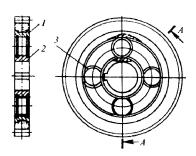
Зубчатый шевер для обработки колее низкой точности: 1— наружная втулка: 2— внутренняя втулка: 3— кольцевые рессоры
